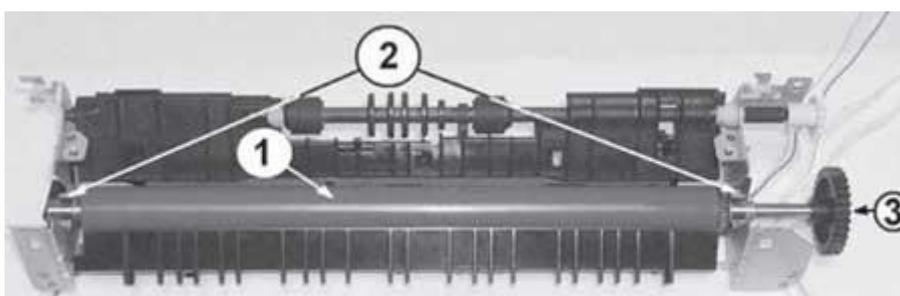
Резиновый вал в сборе с шестерней привода и бушинги резинового вала
